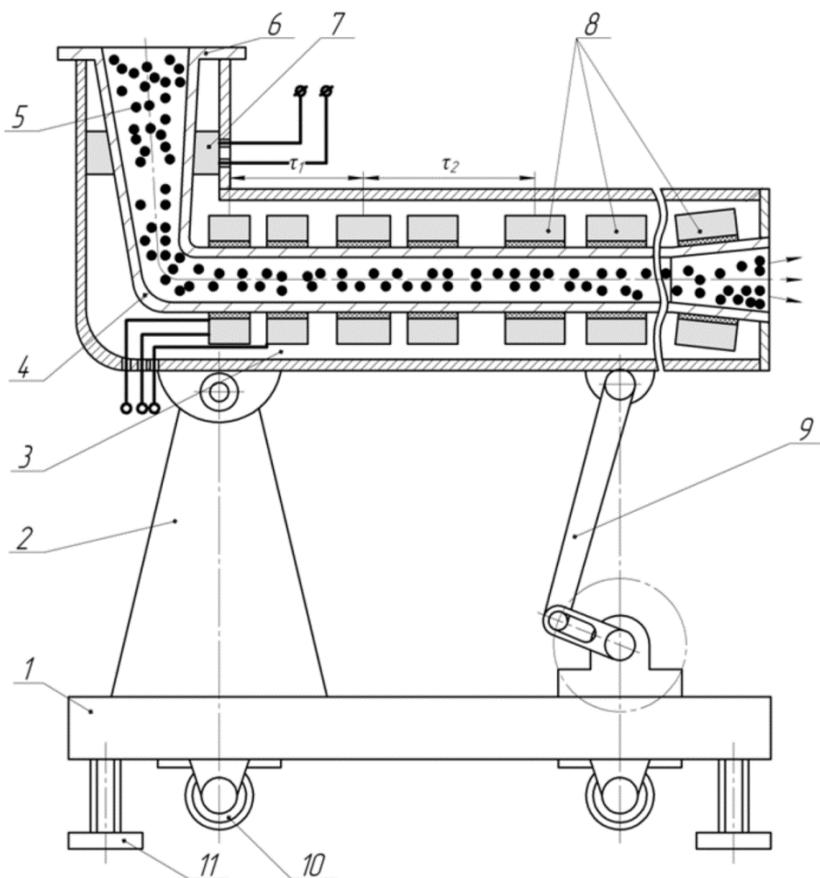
Электромагнитный дробеметный манипулятор: 1 – основание; 2 – опорная тумба; 3 – магнитопровод; 4 – направляющая труба; 5 – дробь; 6 – воронка; 7 – регулятор подачи дробы; 8 – катушки электромагнитные; 9 – кривошипно-шатунный механизм; 10 – ролик; 11 – опора
